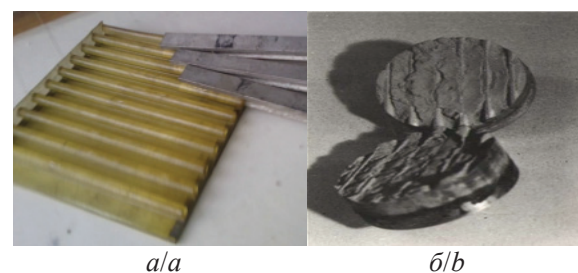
Фотографии профильного теплозащитного покрытия (а) и образца скрепления диаметром 115 мм с инертным твердым топливом (б)
